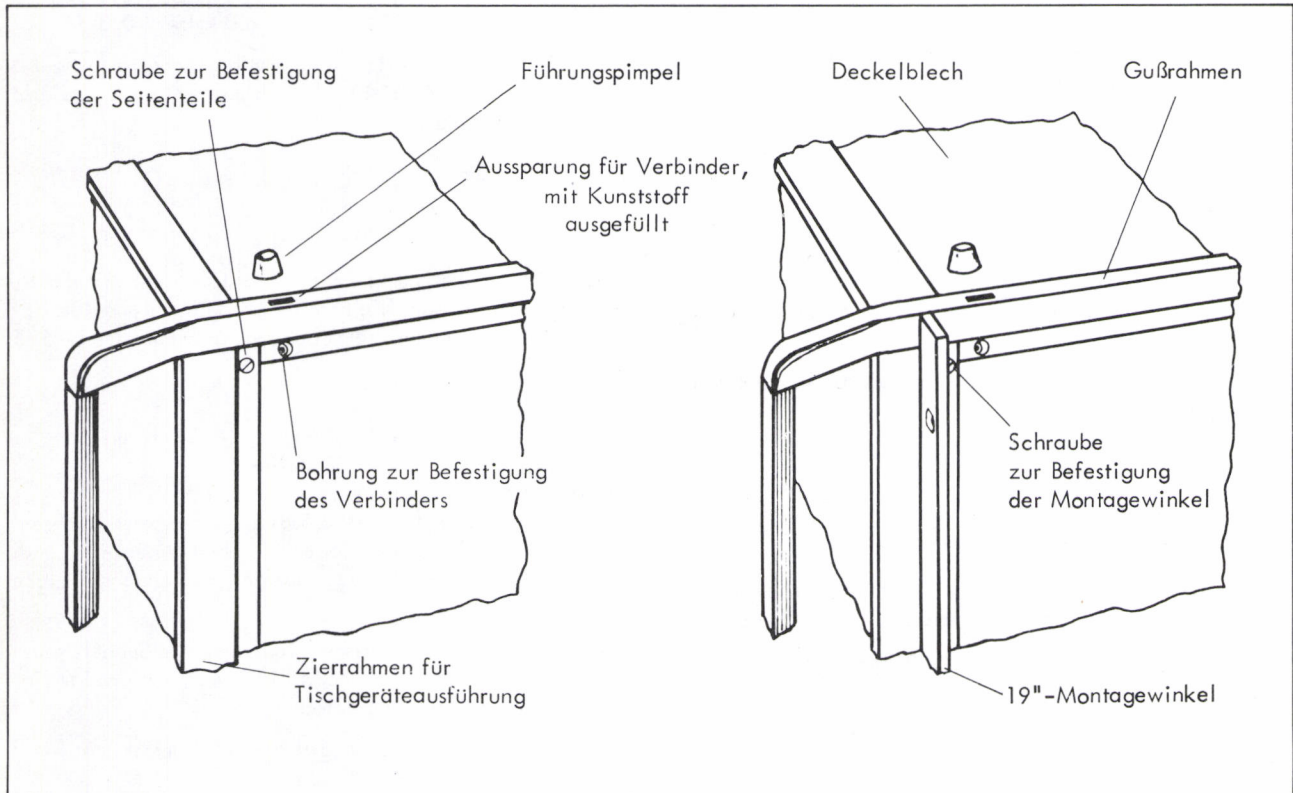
Anbringen der Montagewinkel für die Einschubausführung
